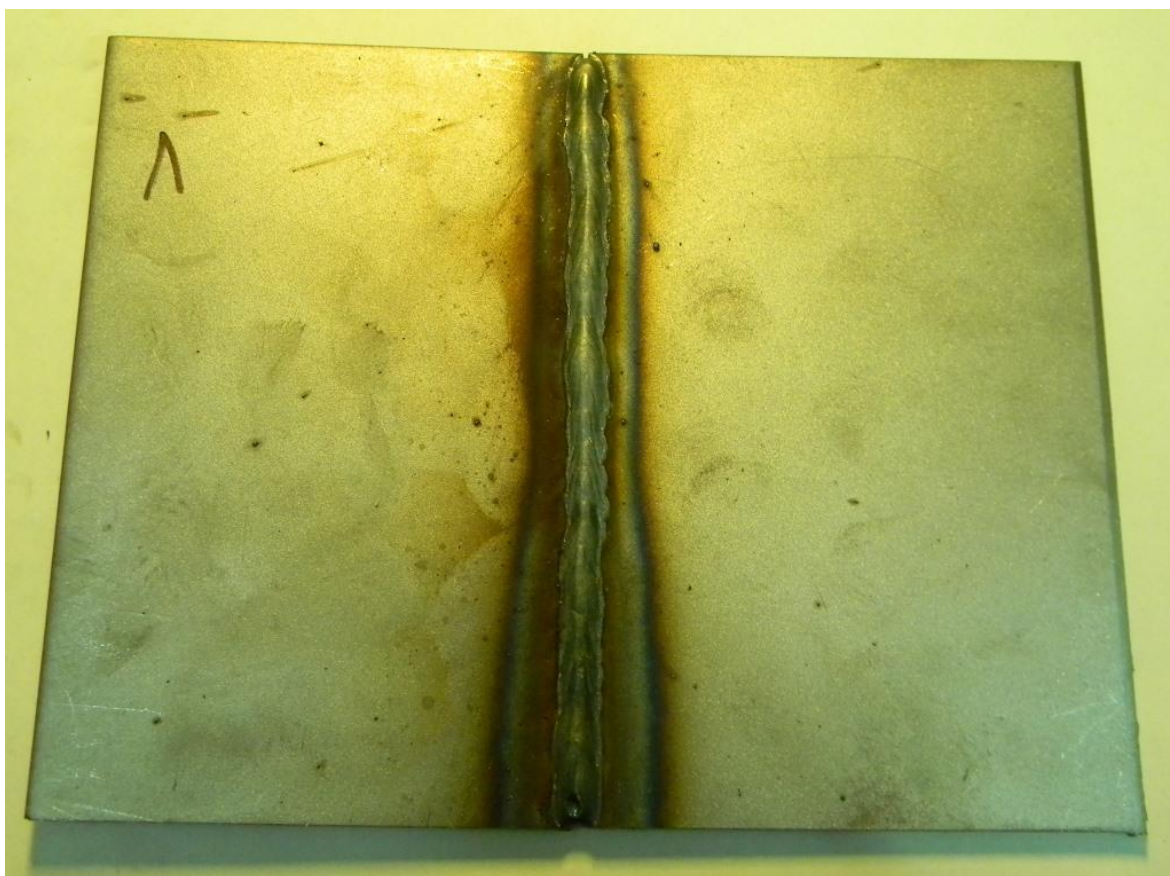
Образец после сварки подготовленный лазерной резкой с EPS
